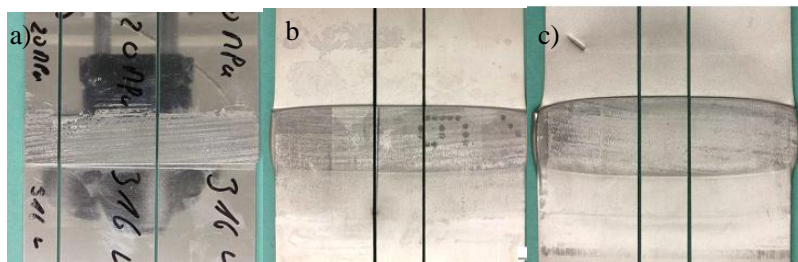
Resultado das amostras soldadas e esquema do plano de corte: a) aço inoxidável 316L soldado com 18 MPa, b) aço inoxidável super duplex UNS 32750 soldado com 30 MPa e c) aço inoxidável duplex UNS 31803 soldado com 30 MPa.
